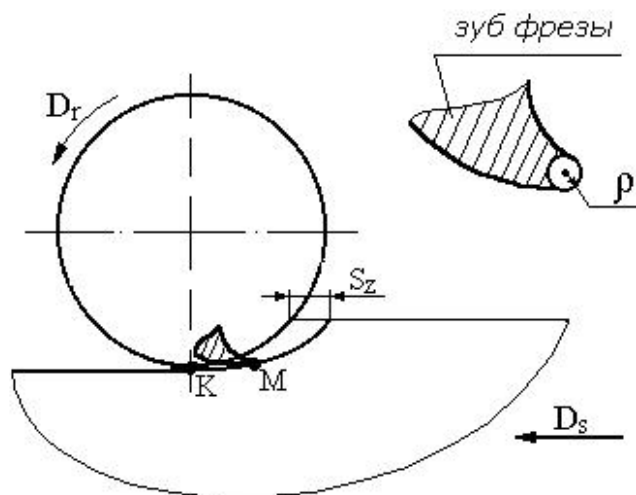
Схема врезания зуба фрезы в заготовку при встречном фрезеровании
